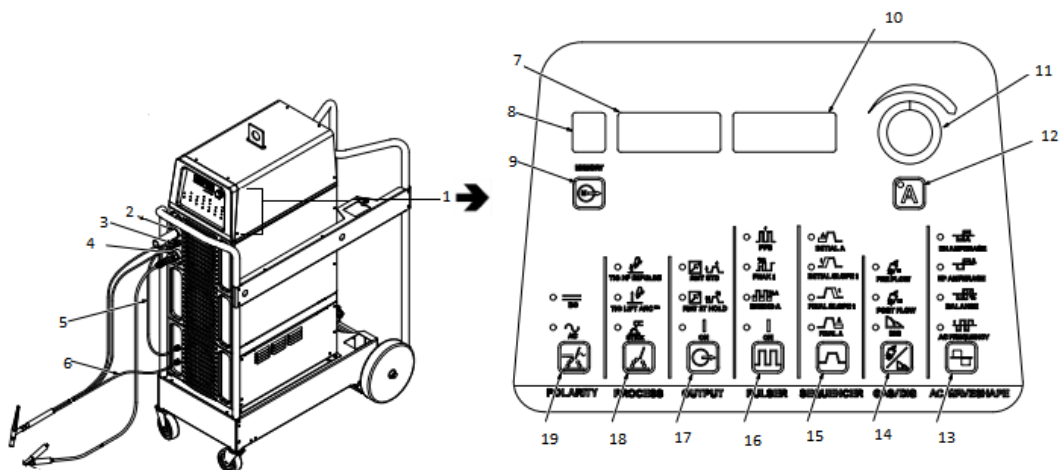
schéma du poste de soudage Miller Dynasty 350,700 Maxstar 350,700.
